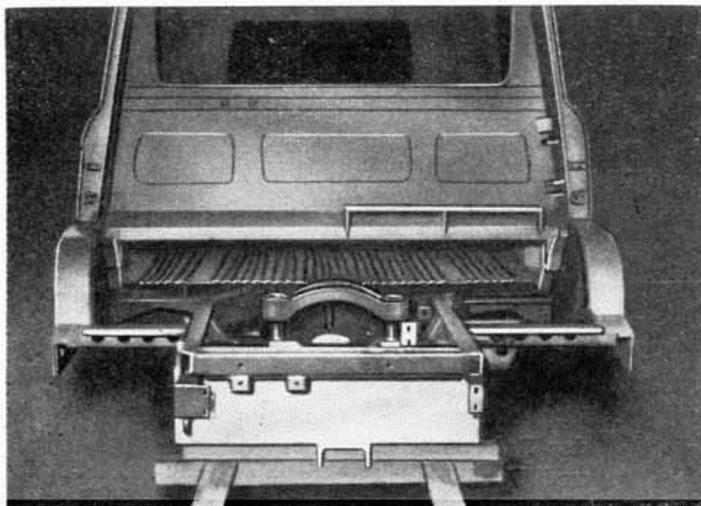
Wagenkörper mit eingelegter Rahmengabel
